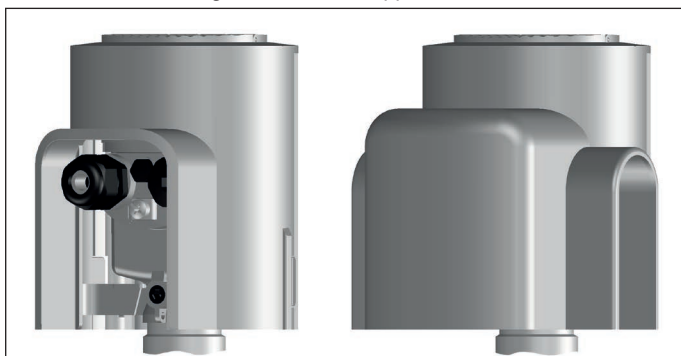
Wetterschutzhaube in verschiedenen Ausführungen
